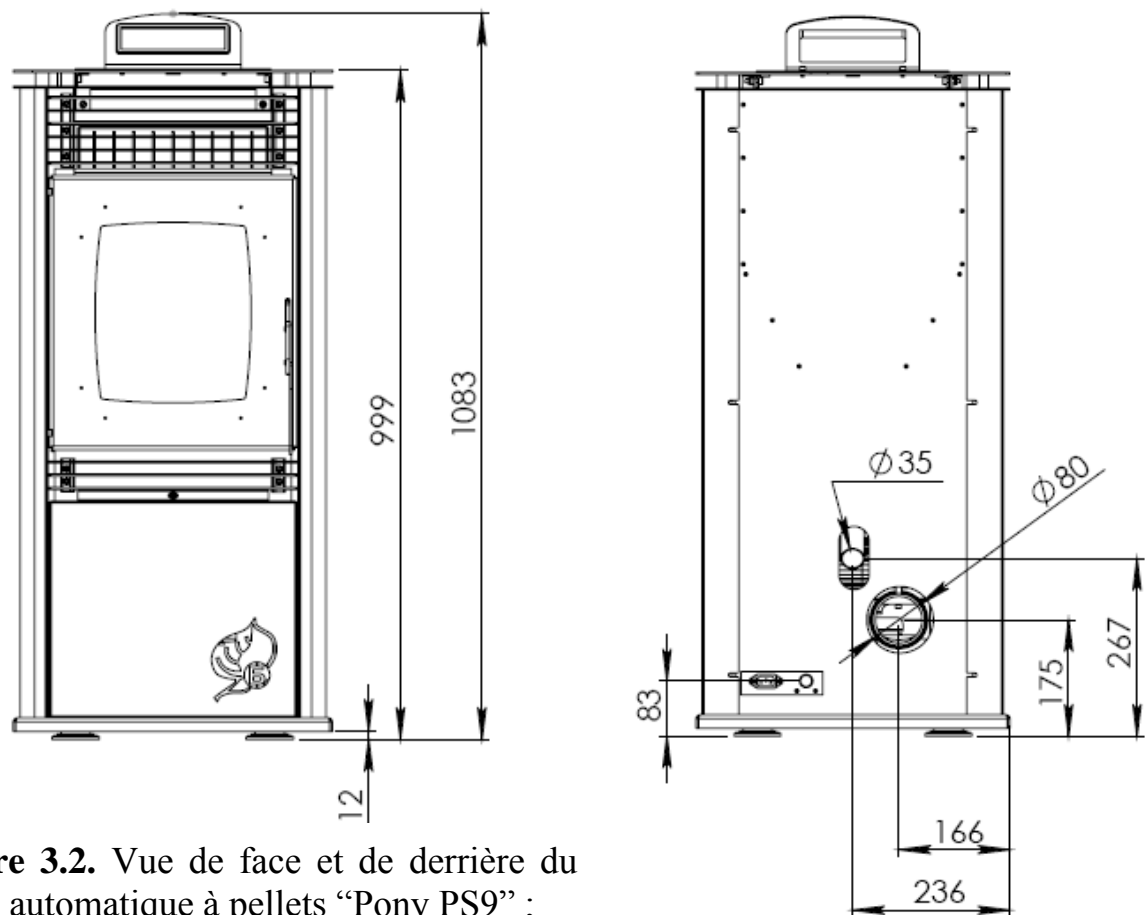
Vue de face et de derrière du poêle automatique à pellets “Pony PS9” ;
